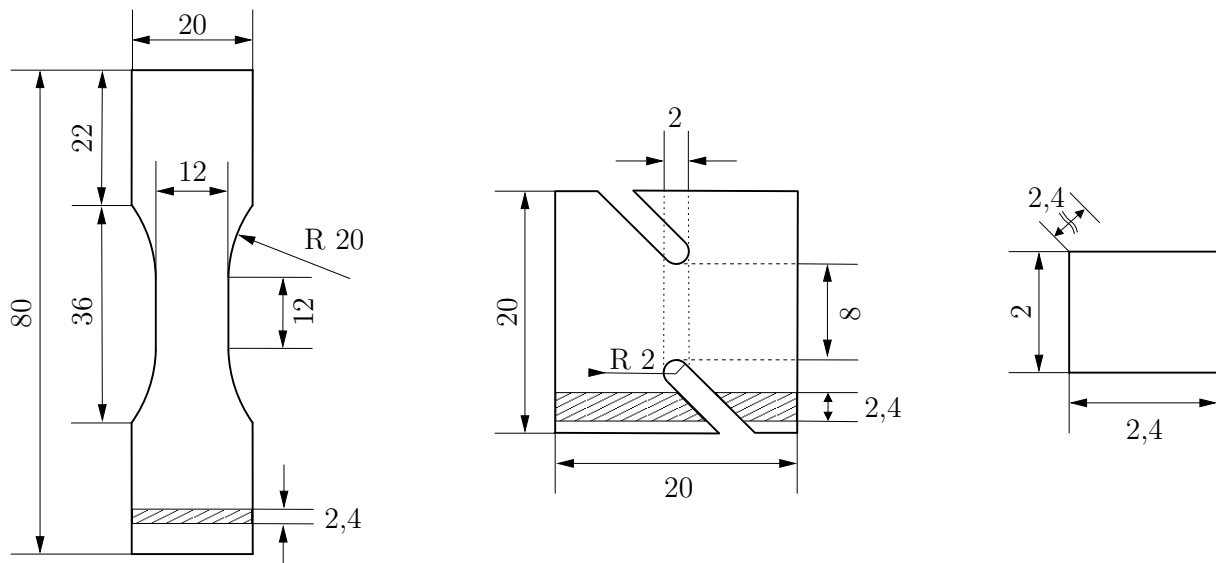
Probekörpergeometrien für die thermomechanischen Charakterisierungsversuche: Zugprobe vom Typ LBF BZ12 (links), Schubprobe vom Typ LBF Z-Probe (mittig) und Druckprobe (rechts). Die Abmessungen sind in [mm] angegeben.
